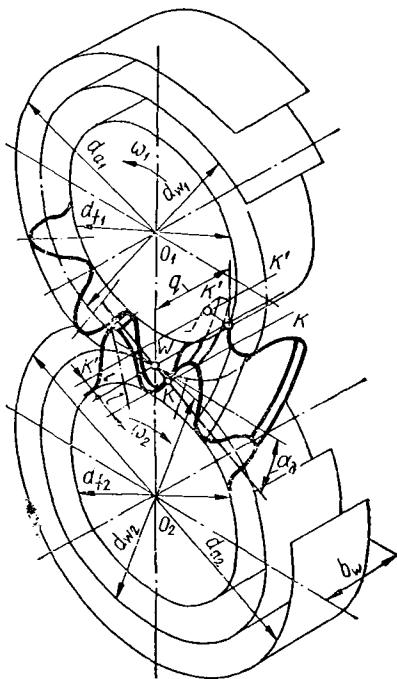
Зубчатый механизм с двумя линиями зацепления
